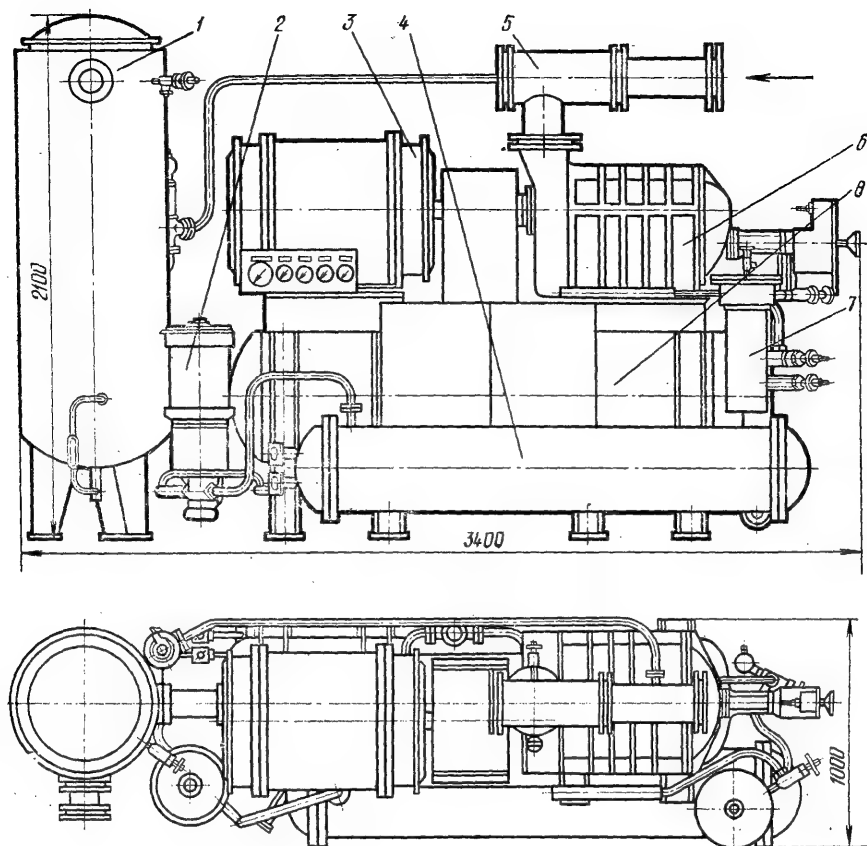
Судовой винтовой компрессорный агрегат 5BX-350/5FC:
